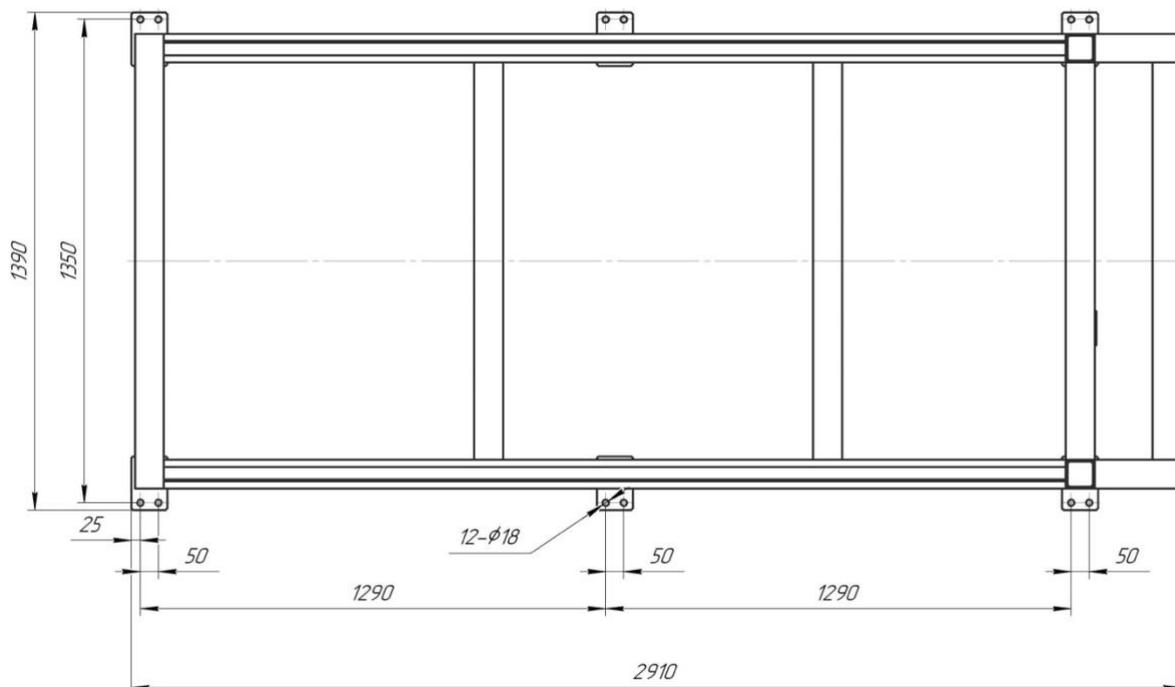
Схема расположения присоединительных отверстий стойки наполнителя биг-бэгов для установки на жестком основании.
